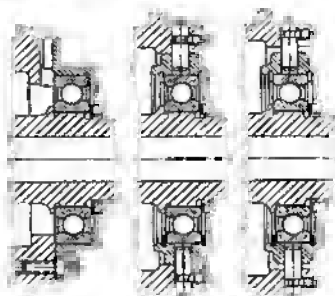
Centrado por rayo de cojinetes de contacto rodante
